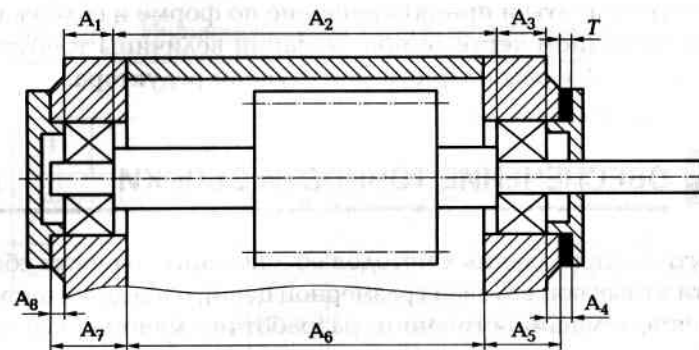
Сборочный чертеж с осевым зазором и компенсатором
